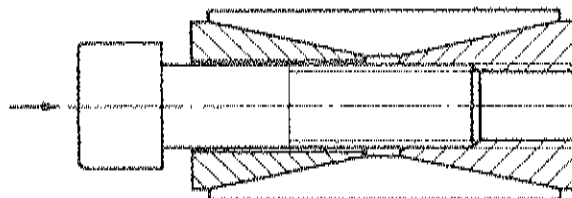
Entspannt der hintere Druckring nicht selbsttätig, so werden die Schrauben um einige Gänge herausgedreht. Nach einigen leichten Schlägen gegen die Schraubenköpfe springt der Druckring nach hinten.
